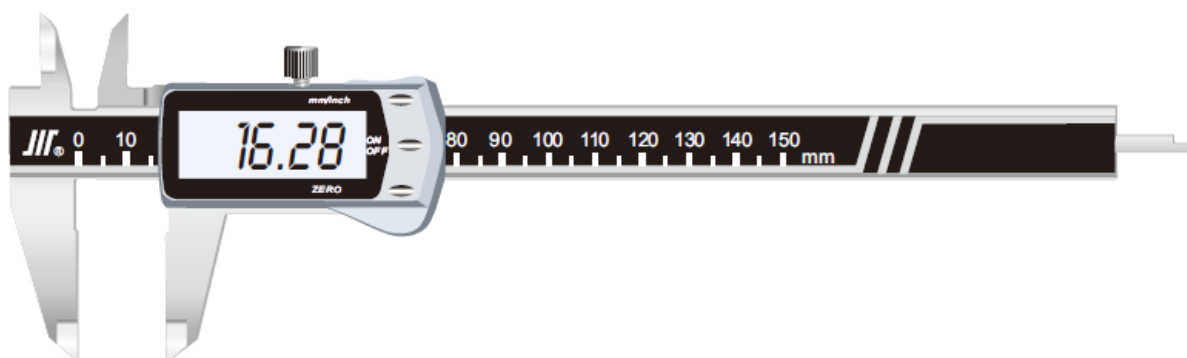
Общий вид штангенциркулей модели ШЦЦ-I
